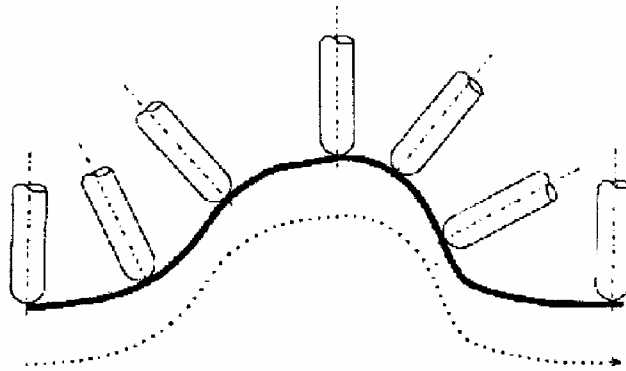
Angle de conduite en usinage sur machine outil à 5 axes, [51].
